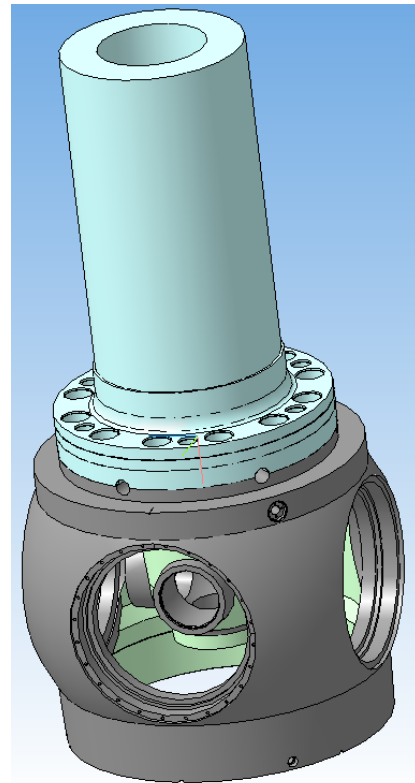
3D модель фланцевого з'єднання валу турбіни і корпусу робочого колеса
